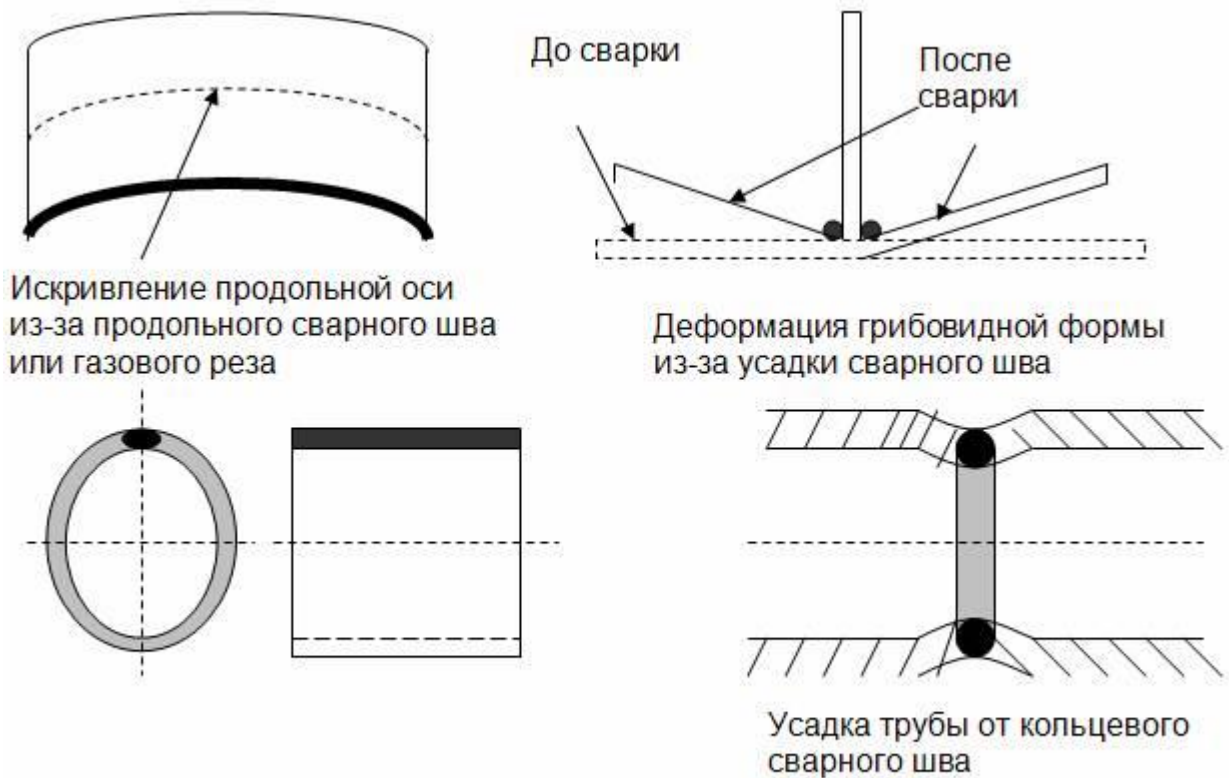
Примеры деформаций деталей при сварке и резке.
